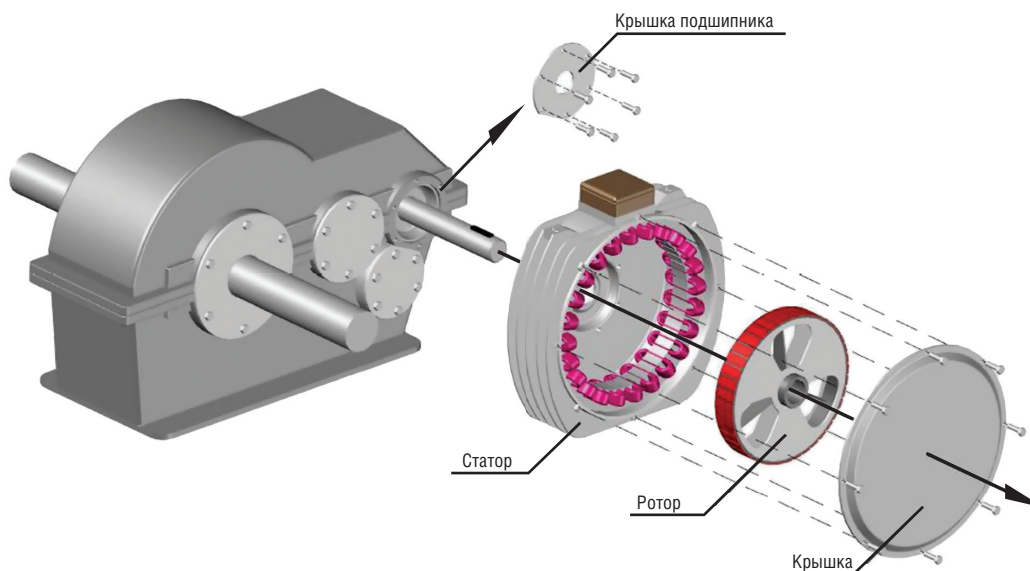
Основные элементы двигателя и схема его установки на редукторе
